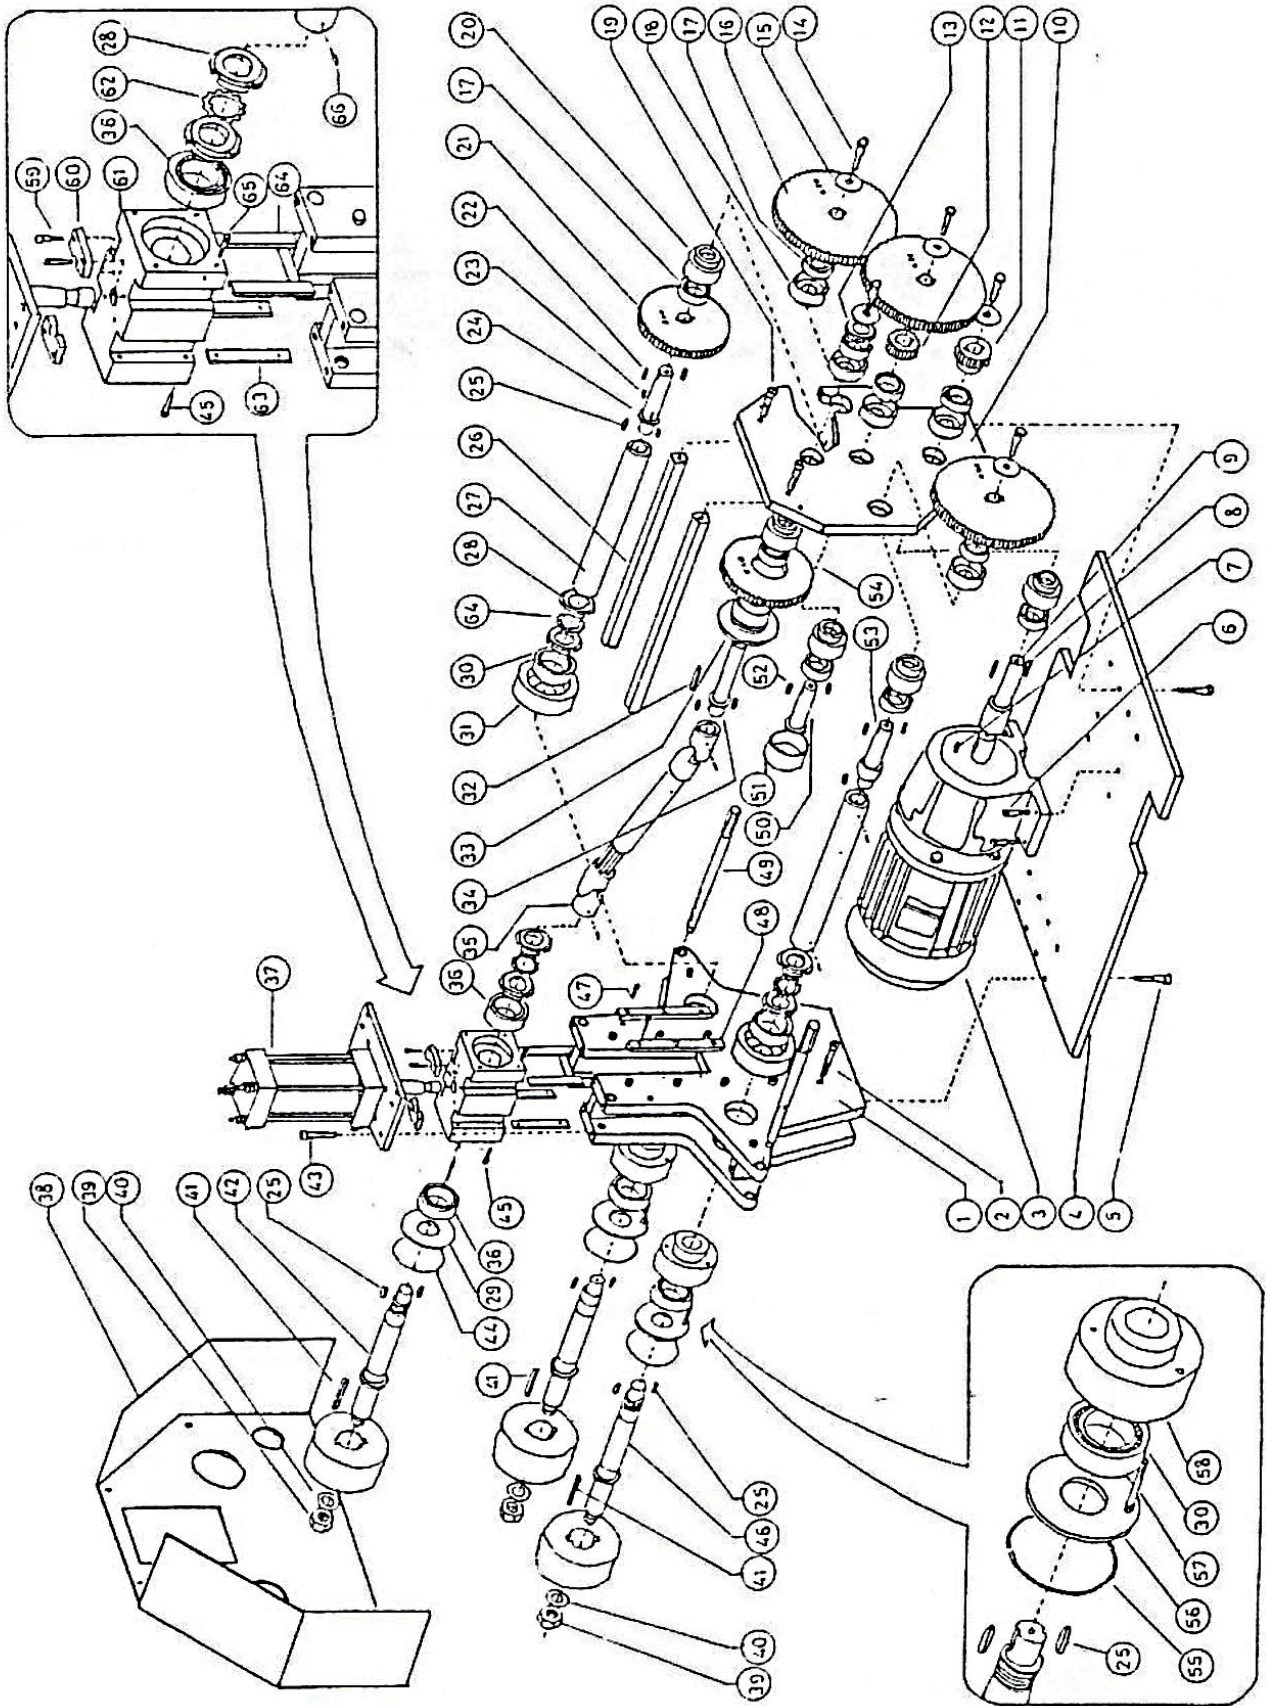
Dessin des pièces détachées 2 - PRM 50 FH
